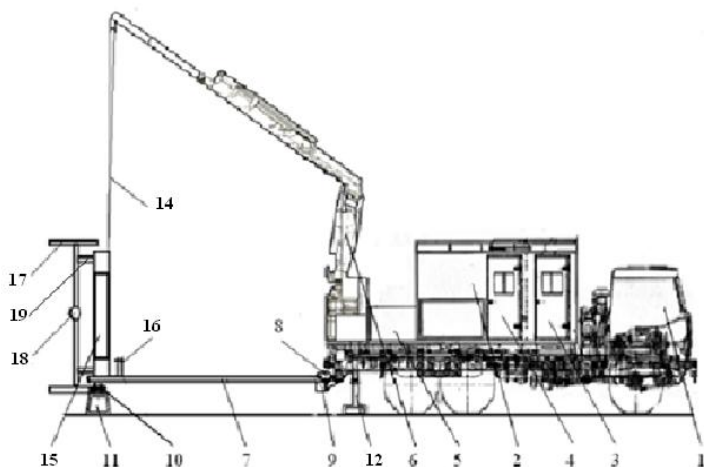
Установка подразобранного автомобиля на разборную конструкцию:
